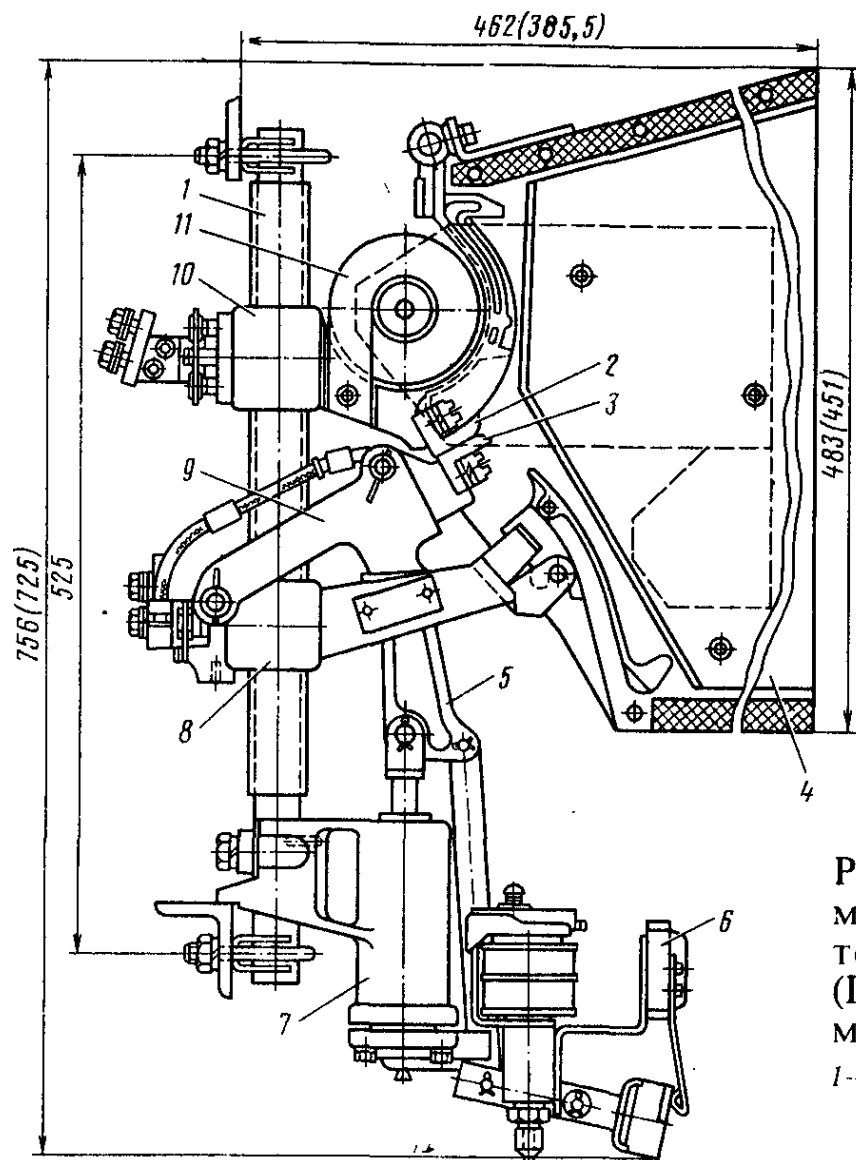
Электropневматический контактор ПК-41 - ПК-46 (ПК-31 - ПК-36, размеры в скобках):
